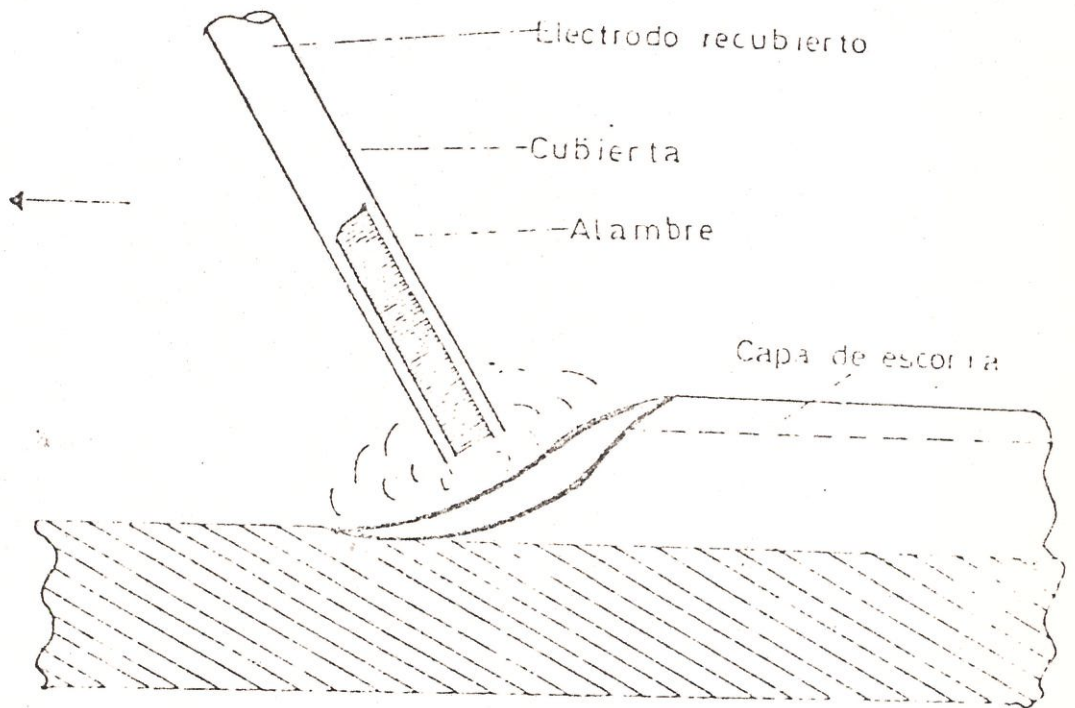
SOLDADURA POR ARCO CON ELECTRODO REVESTIDO (14)
